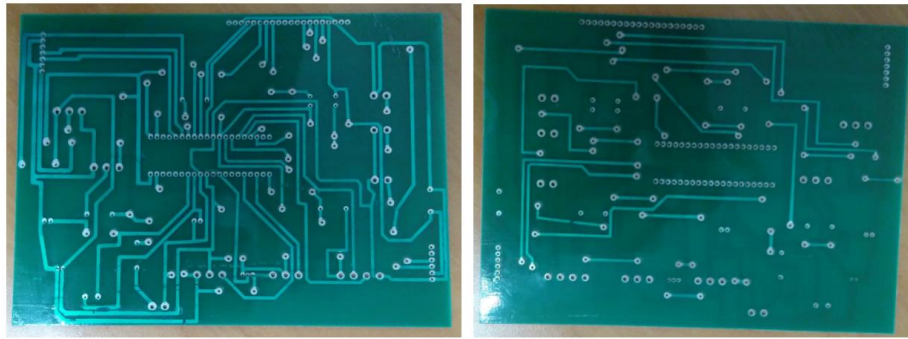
Diagrama del Diseño PCB para imprimir diseñado en Proteus.
